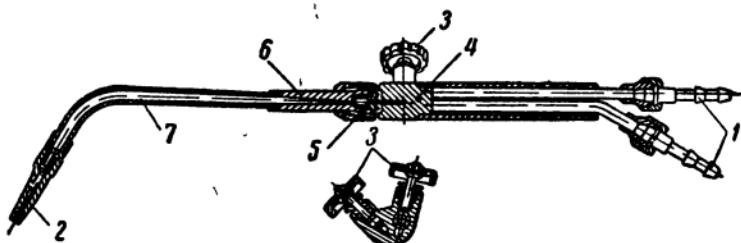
Ацетилено-кислородная сварочная горелка типа СУ-48:
